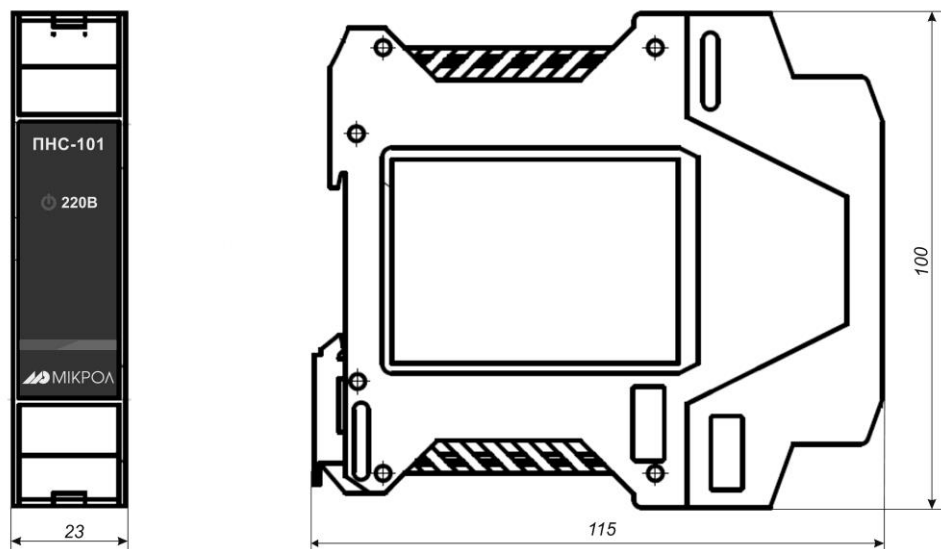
Зовнішній вигляд і габаритні розміри ПНС-101
